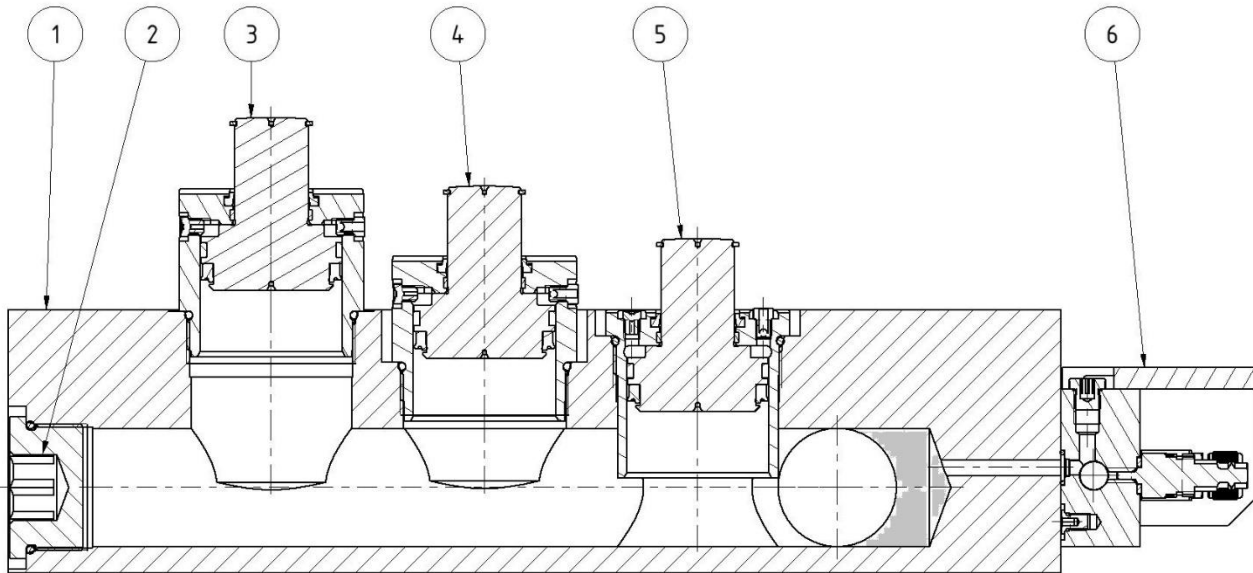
Schnittdarstellung einer Tankplatte mit Bezeichnung der Bauteile
